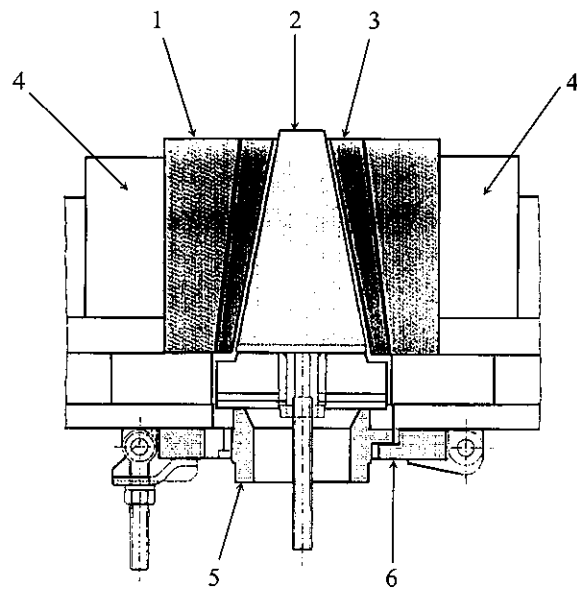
Установка продувочной пробки в днище сталеразливочного ковша:
